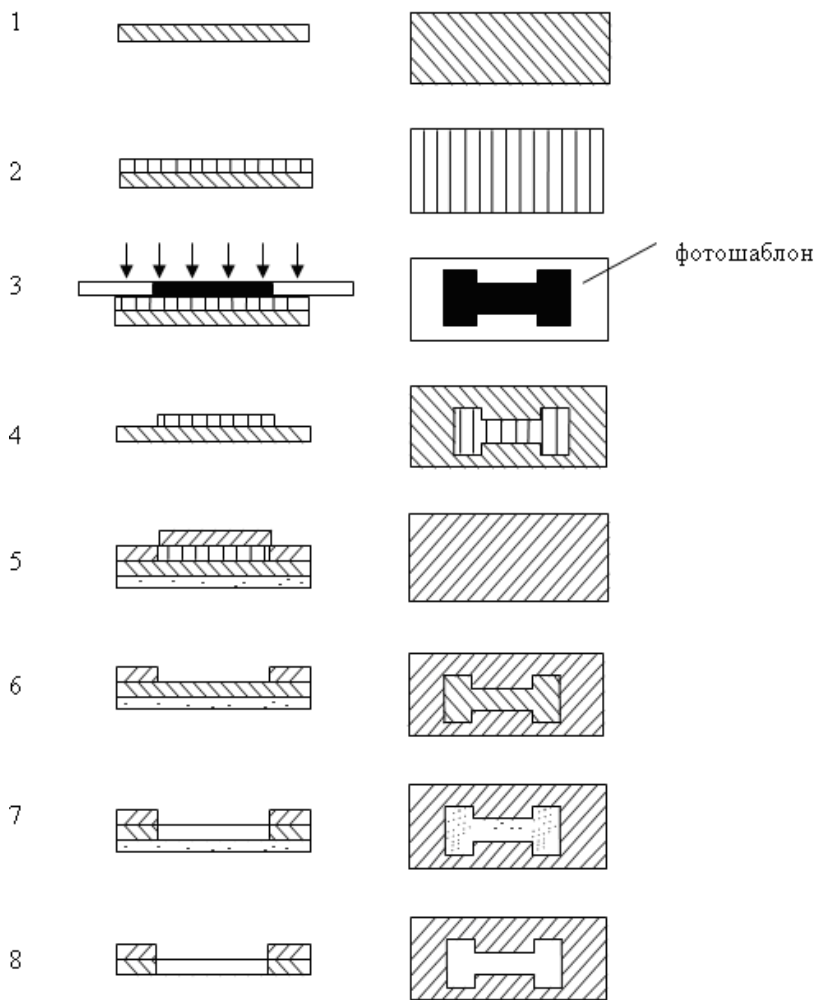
Технологический маршрут изготовления биметаллической свободной маски: 1 – лента бериллиевой бронзы; 2 – нанесение фоторезиста; 3 – экспонирование; 4 – фотообработка; 5 – нанесение слоя защитного лака с обратной стороны ленты и осаждение никеля на незащищенные участки; 6 – снятие фоторезиста; 7 – травление бериллиевой бронзы; 8 – снятие защитного лака
